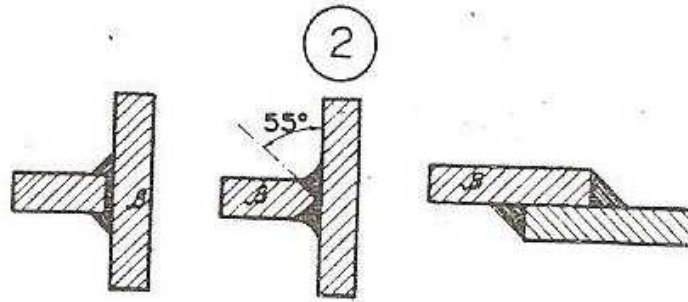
Soldadura en los ángulos entre materiales.
